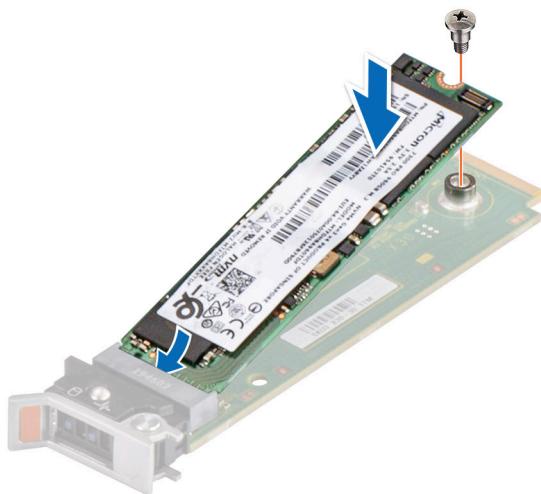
Installieren des M.2-SSD-Laufwerks
